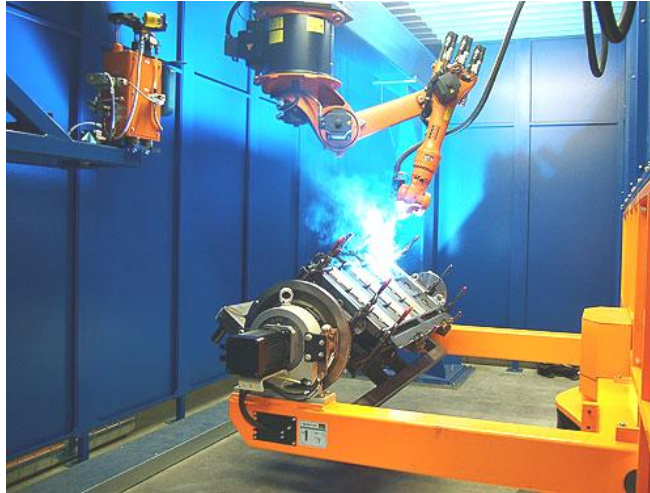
Сварочный робот с вращающейся оснасткой.
